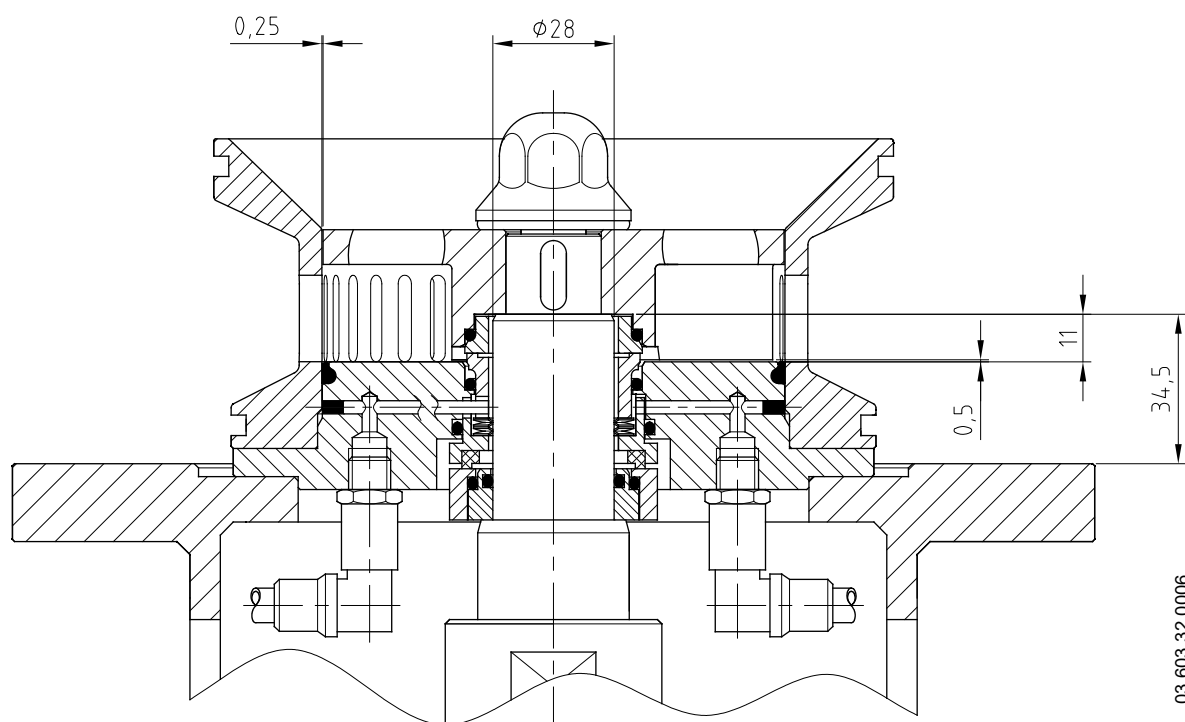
Dimensions de montage pour la double garniture mécanique de taille ME-6103/6105/6110 RE.
